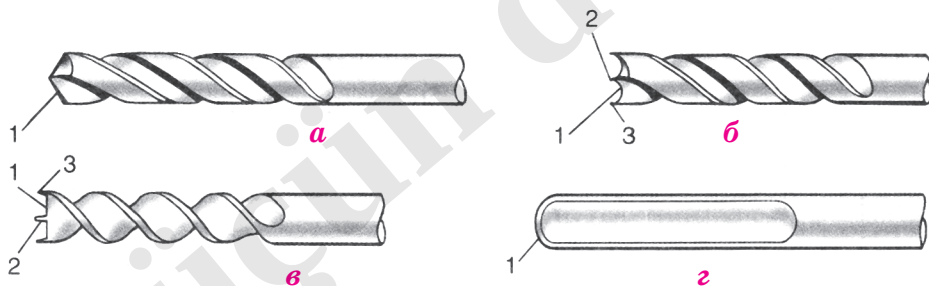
Сверла: а – спиральное; б – центровое, в – шнековое, г – ложечное (1 – режущая кромка; 2 – центр; 3 – подрезатель)
